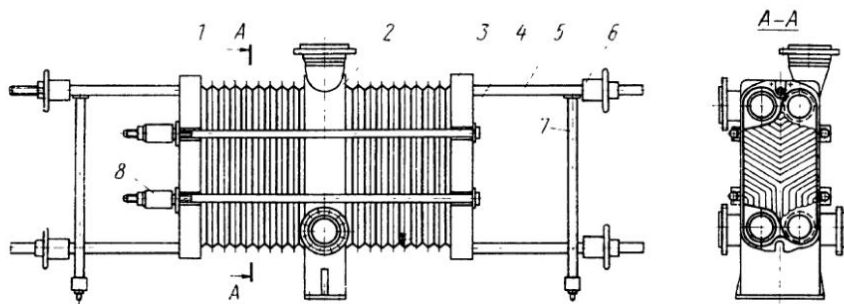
Пластинчатый полуразборный двухсекционный конденсатор на раме с центральной неподвижной опорой:
